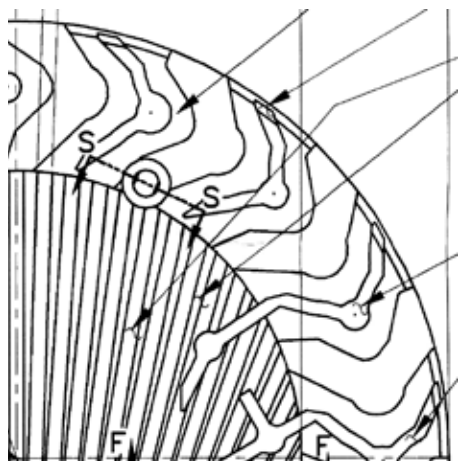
Фрагмент чертежа конструкции оптической камеры адресно-аналогового дымового извещателя
